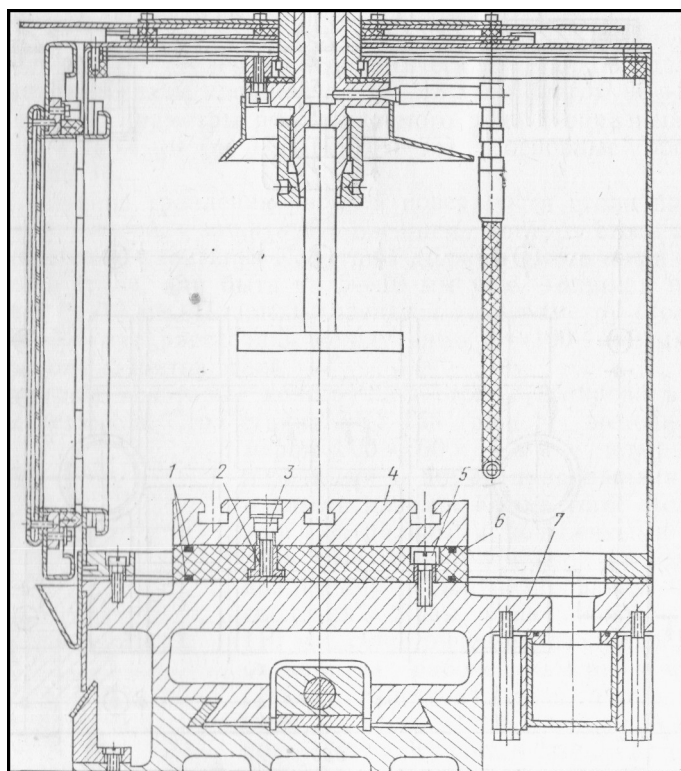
Робоча камера електрохімічного копіювально-прошивного верстата моделі 4422: 1 - ущільнення; 2 - гайка; 3 - гвинт; 4 - інструментальна плита; 5 - гвинт; 6 - ізолятор; 7 рухомий стіл
